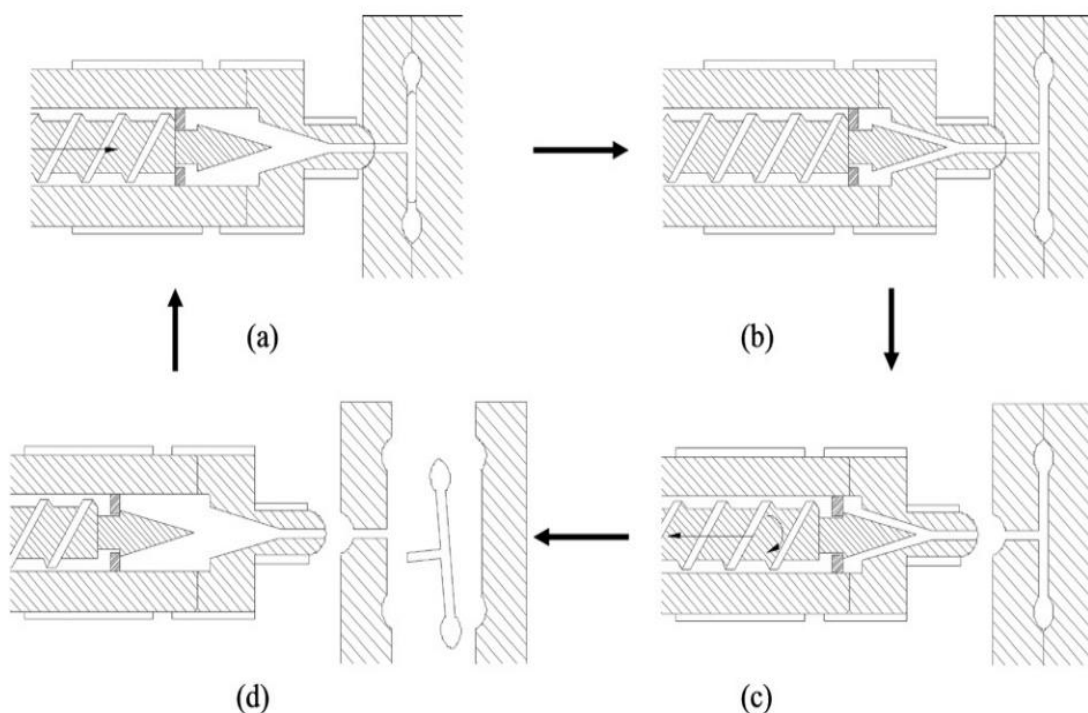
Ciclo de injeção. a) Fecho de molde ; b) enchimento; c) compactação; d) abertura do molde e extração [4]
